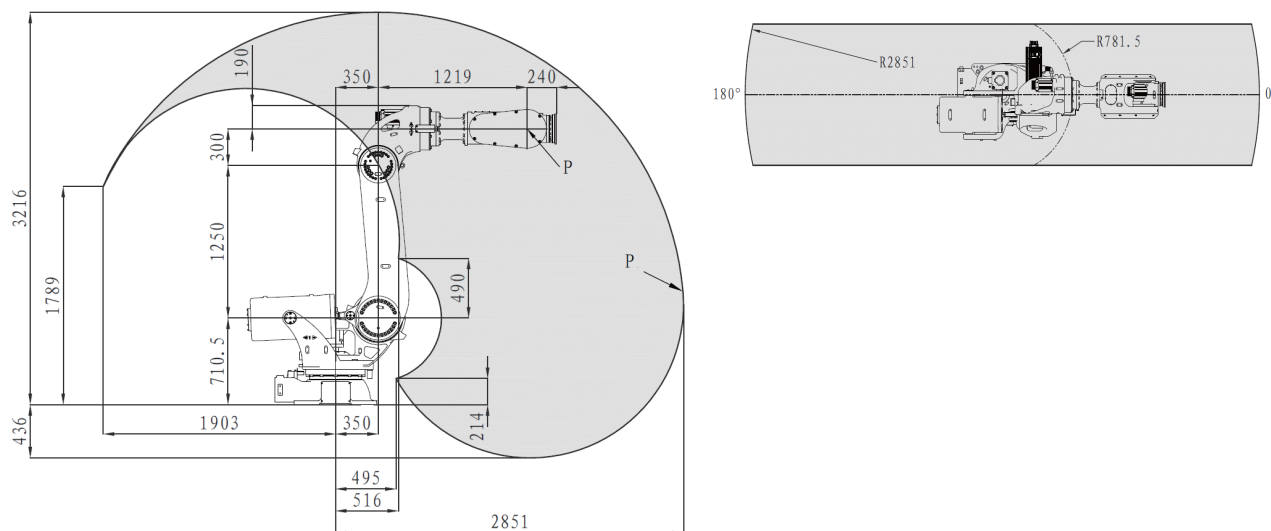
Габаритные чертежи робота-манипулятора SR175-2700.
